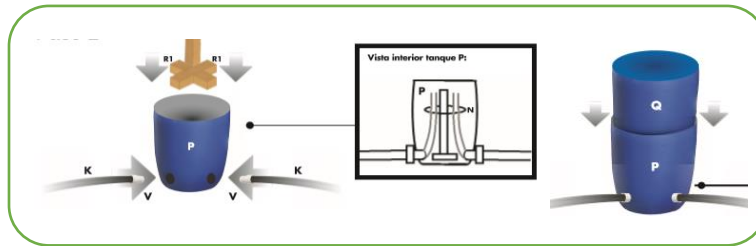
Montaje tanque de almacenamiento materia orgánica.
